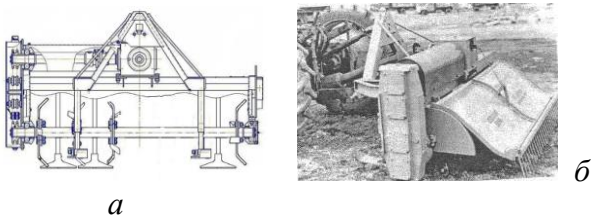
Схема фрези ФНС-1,5А – а і загальний вигляд – б.
